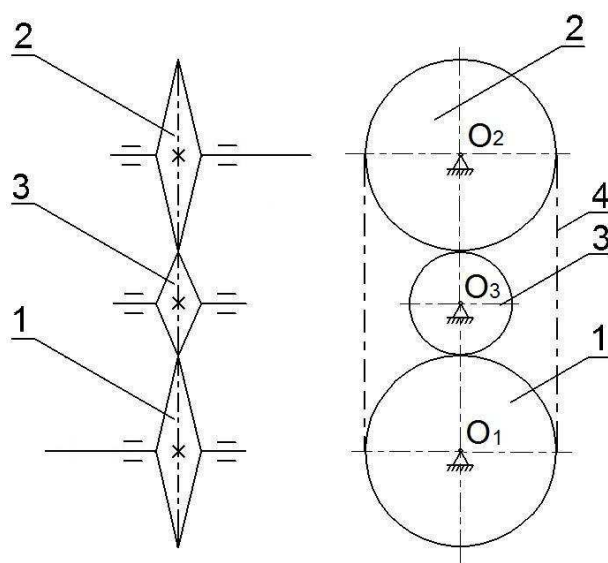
Схема зубчато-цепной передачи-привод с однорядной цепью
